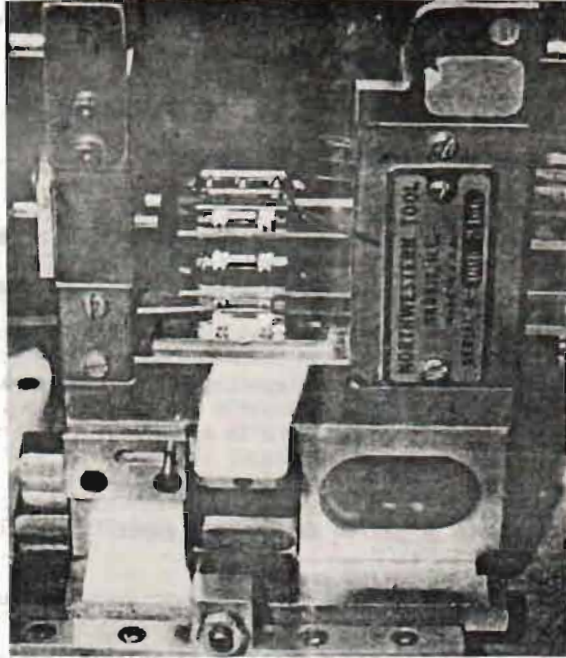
y 25. Montado de las rejillas al soporte para flejado y frizado.
